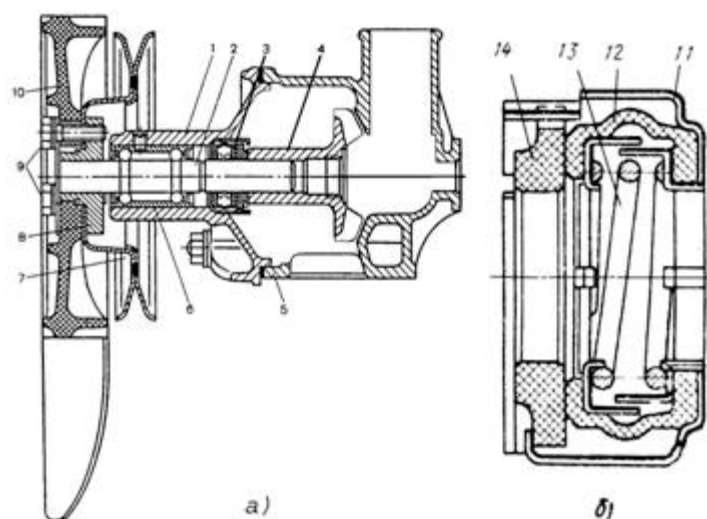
Насос и вентилятор двигателей ВАЗ (а); уплотнитель жидкостного насоса (б)
